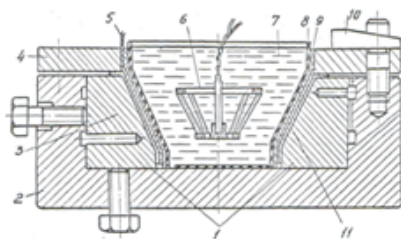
Схема установки для гидровзрывной штамповки с нагревом
